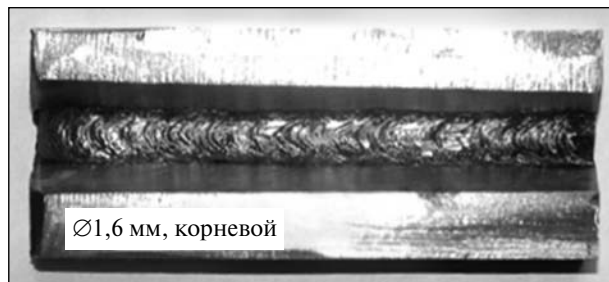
Зовнішній вигляд зварних швів при мокрому підводному зварюванні високолегованої корозійностійкої сталі типу 18-10
